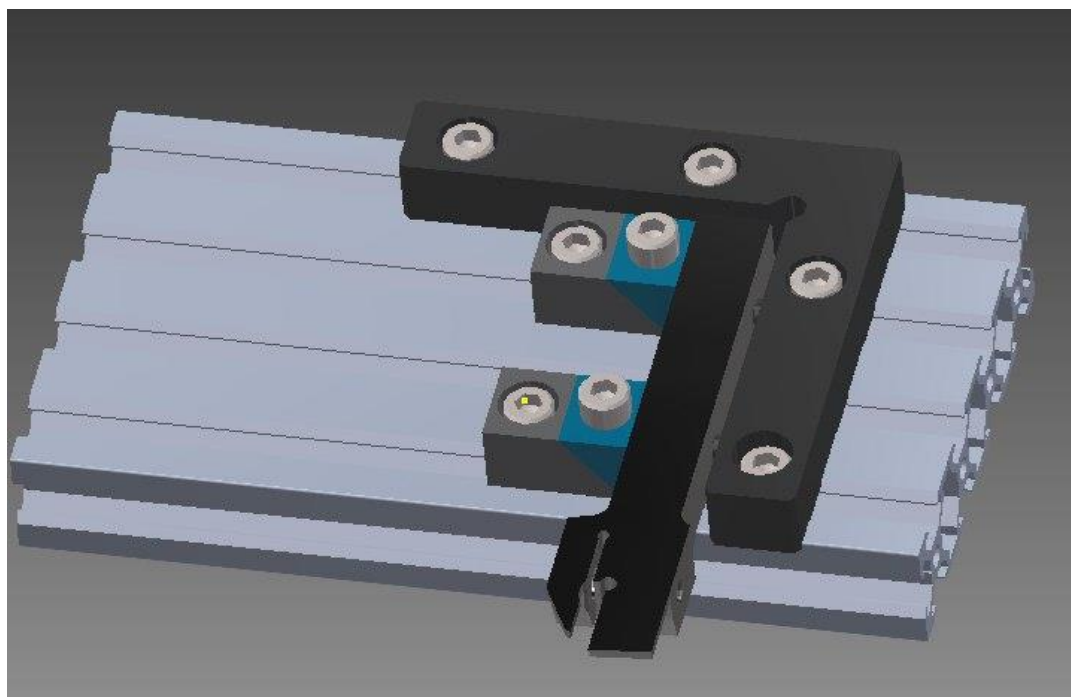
Пристосування для фрезерування пазу під пластину
